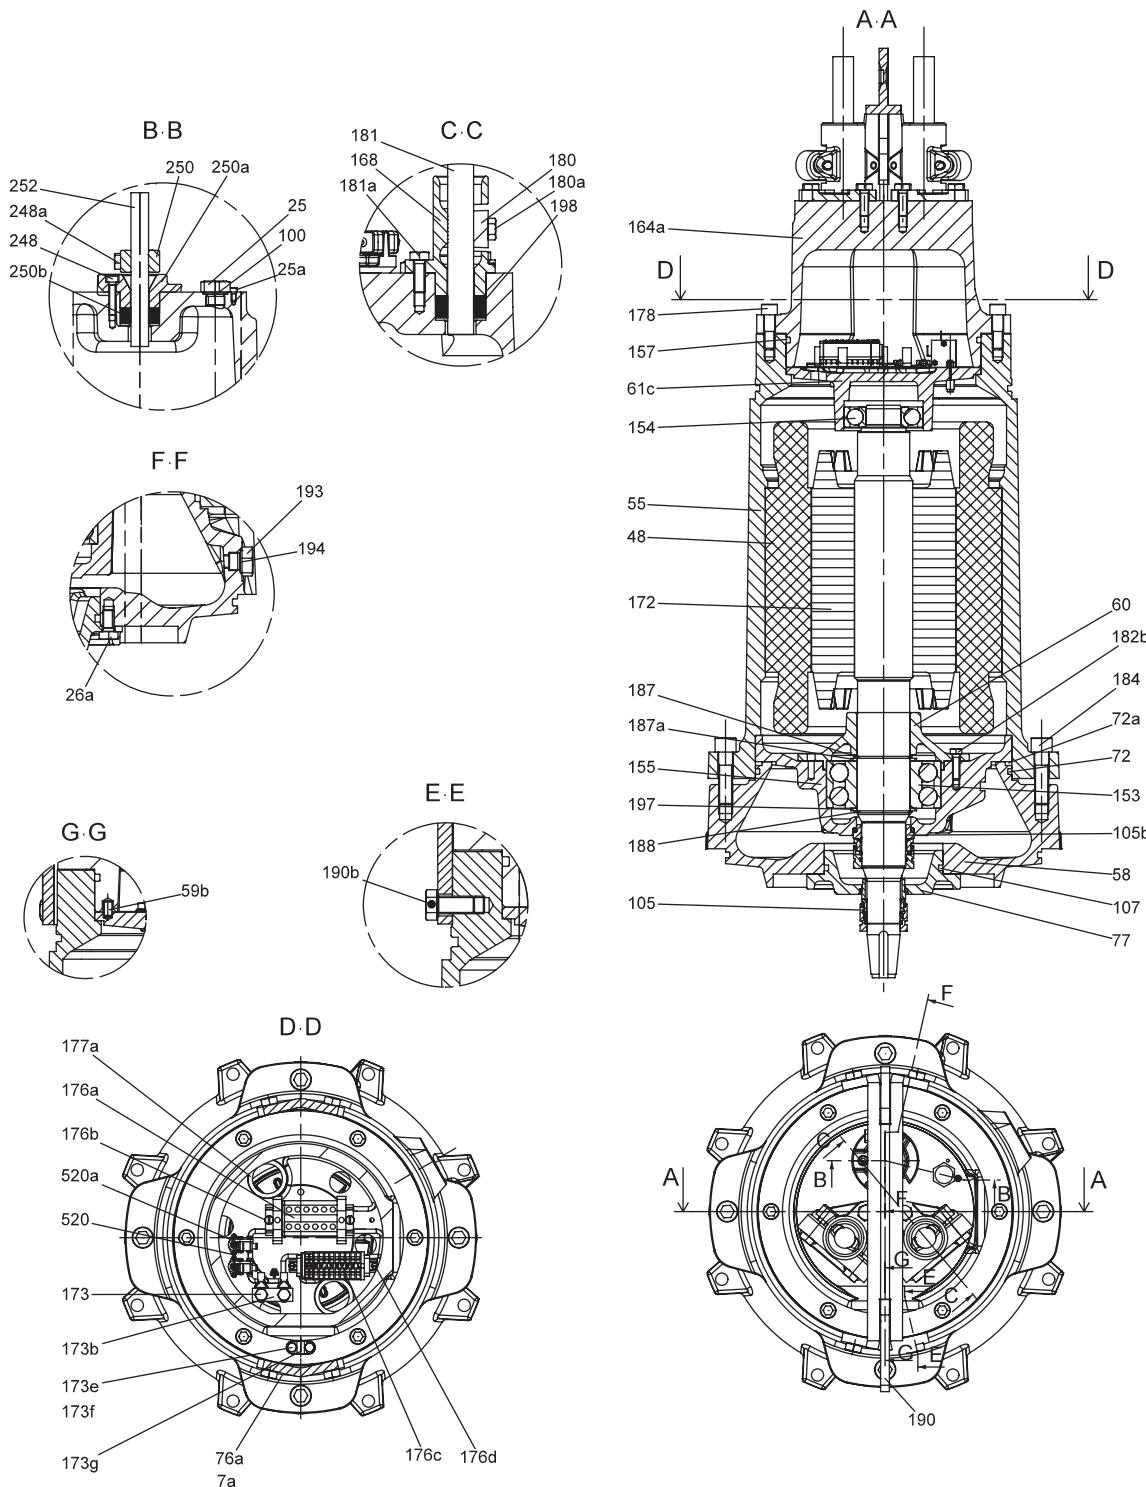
Взрывозащищённый двигатель без охлаждающего кожуха
